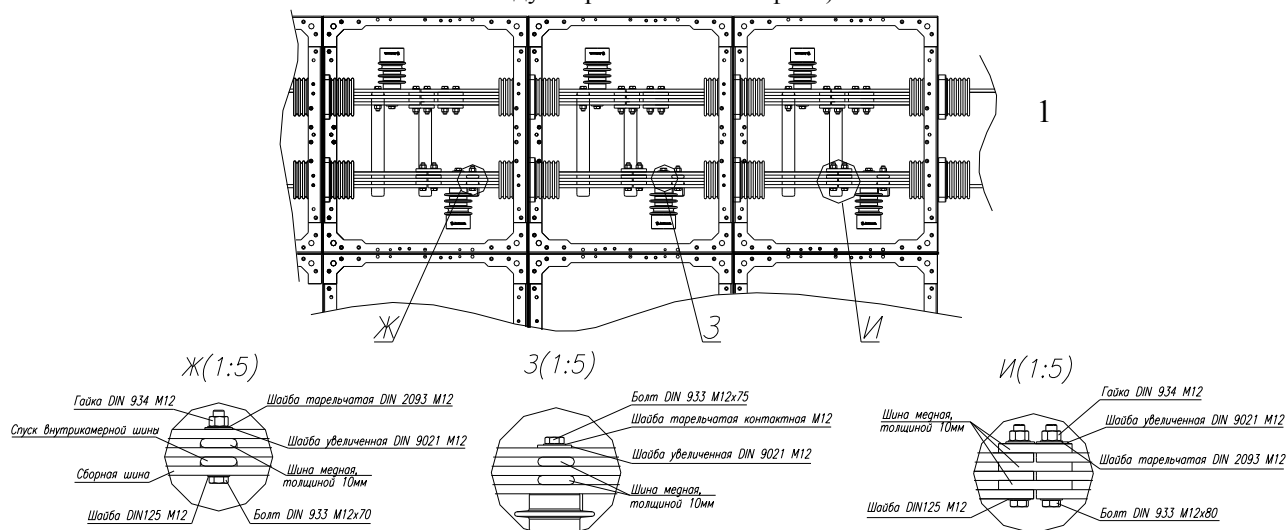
Монтаж сборных шин 3150; 4000А (вид сверху на шкафы КРУ)
